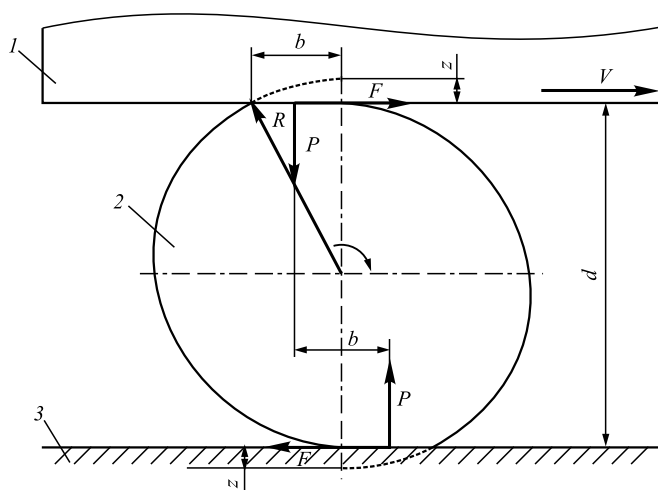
Схема обжатия цилиндра при поперечной обкатке: 1 — подвижная плита; 2 — заготовка; 3 — неподвижная плита
